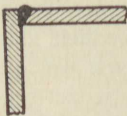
Eckverschweißung zweier Bleche.
